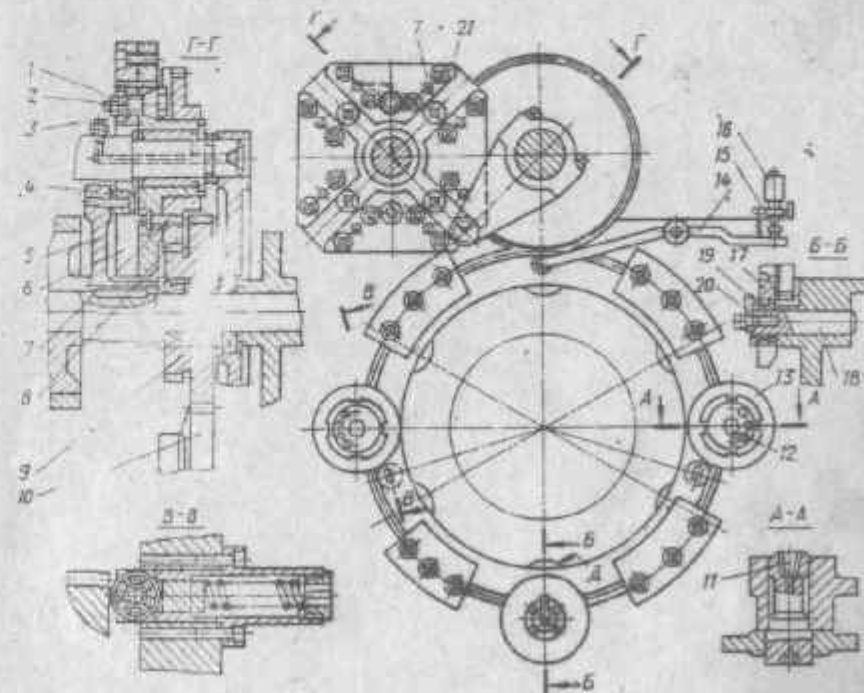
Механизм поворота и подъема шпиндельного барабана
